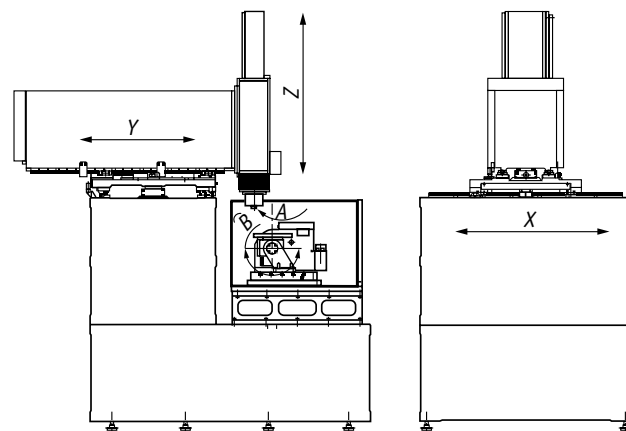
Схема расположения координатных осей копировально-прошивного станка
